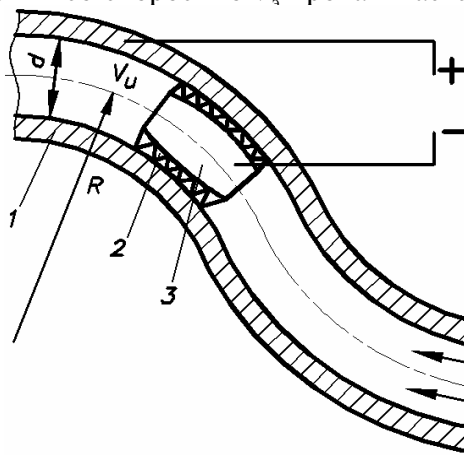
Схема обработки протягиванием внутренней поверхности трубы:
